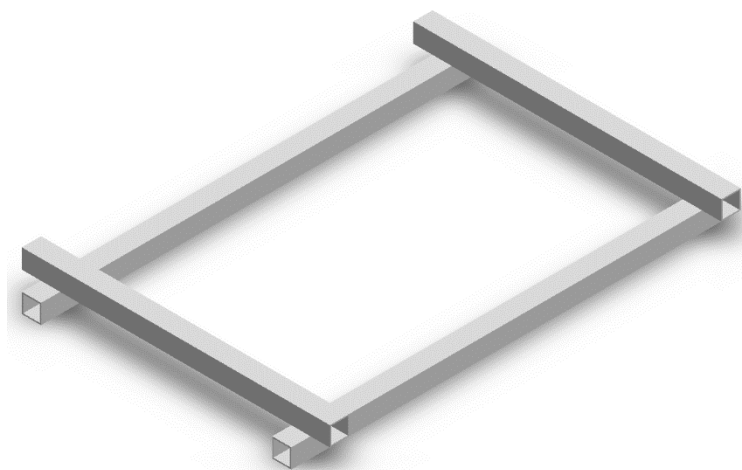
Conjunt 3D del suport amb les parts que el constitueixen.
